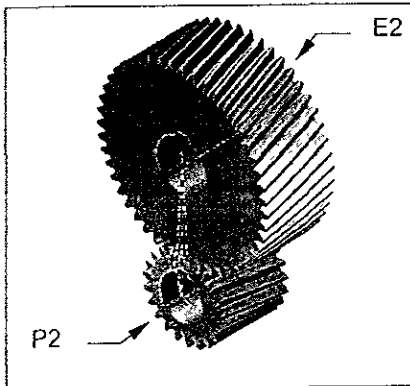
Ensamble del piñón y engrane helicoidal.
